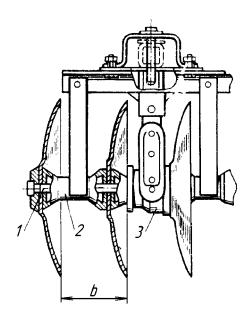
Схема установки сферических дисков в батареи: 1 — квадратная ось; 2 — шпулька; 3 — подшипник
